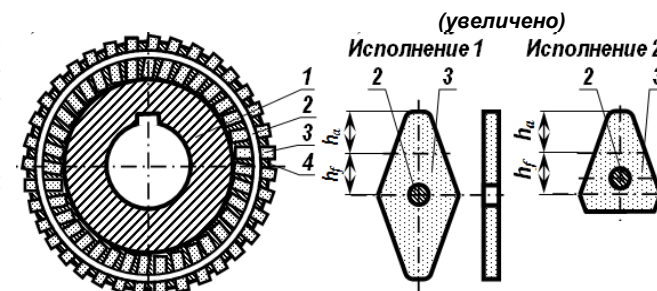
Сборная червячная фреза по патенту Российской Федерации №2169061 с установленным в винтовых канавках на ее корпусе набором из неперетачиваемых режущих пластин и клиньев, закрепленных введенными в их отверстия пружинами и режущие пластины для ее оснащения
